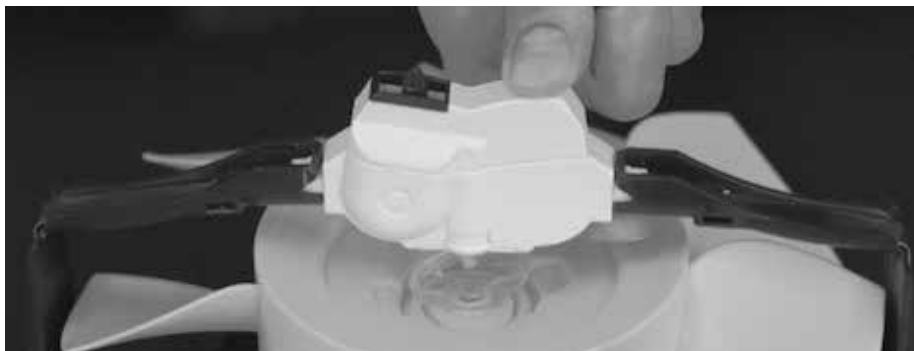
Fig D. ... et le faire remonter dans l'engrenage jusqu'à ce qu'il tienne solidement... Sur les modèles ayant une petite goupille blanche, insérer tout d'abord celle-ci à travers le raccord en caoutchouc puis pousser les deux dans l'engrenage jusqu'à ce qu'ils tiennent
